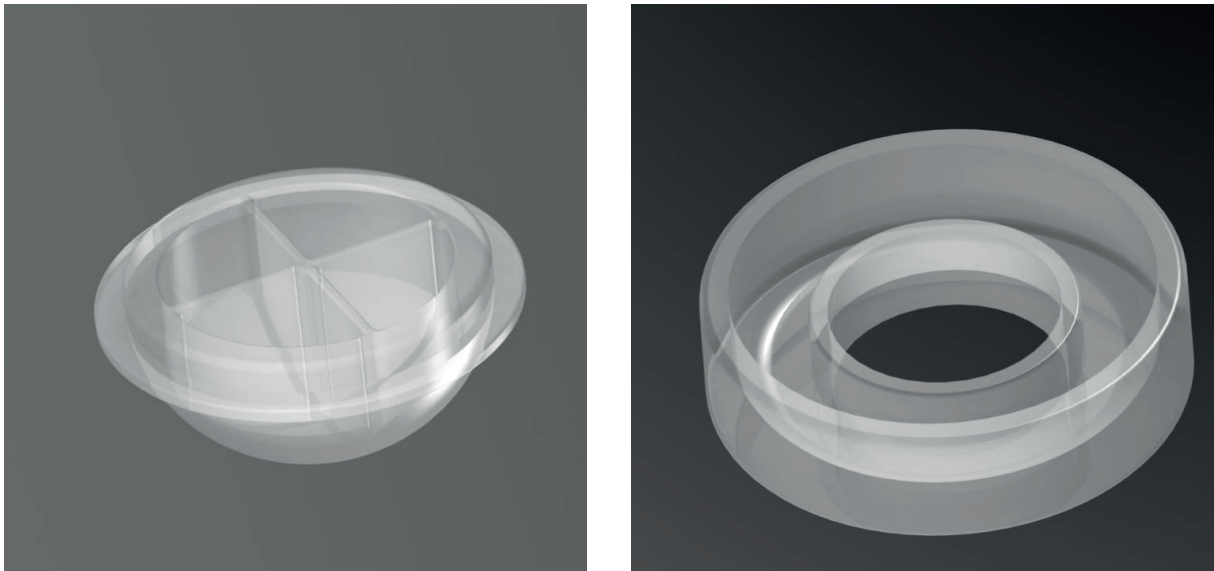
Vista de las piezas por separado de la solución adoptada del diseño estructural.
